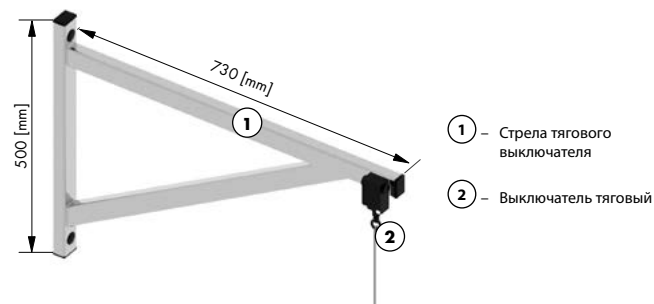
Тяговый выключатель и стрела тягового выключателя.
